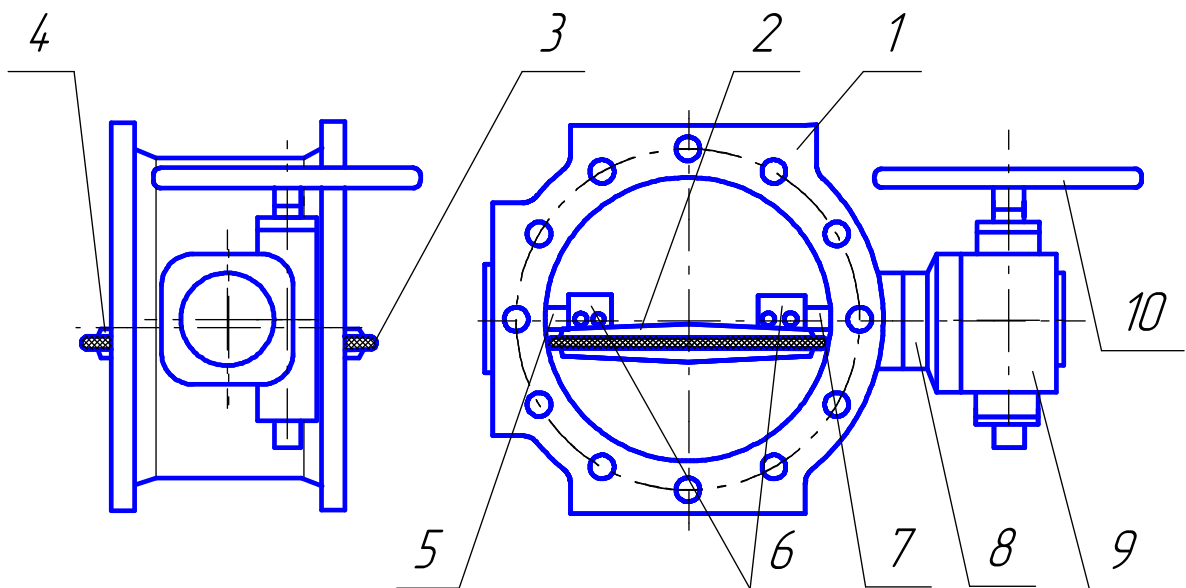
Устройство затвора с ручным приводом и штурвалом
